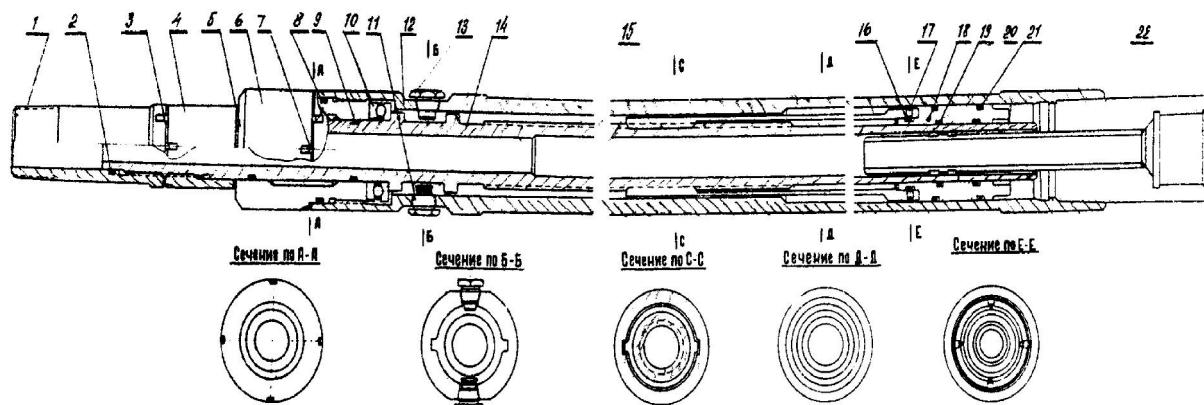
Глубинный вращатель гидropескоструйного перфоратора:
